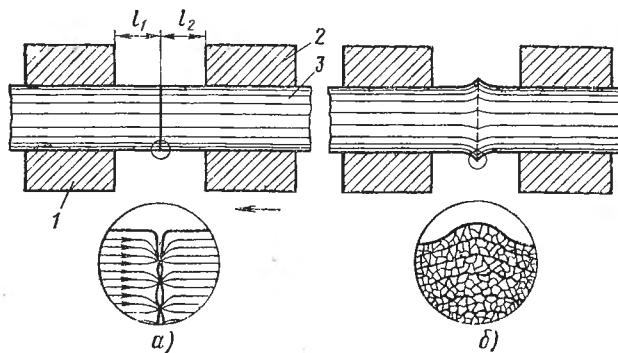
Схемы процессастыковой сварки сопротивлением
